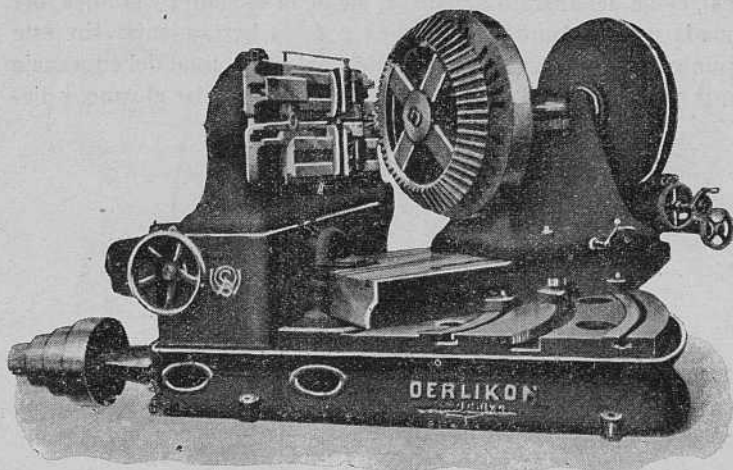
Cepilladora de doble cuchilla para engranajes cónicos.
